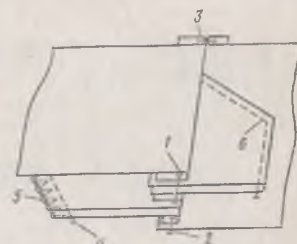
Сборочная схема непрорезного кармана с листочкой
